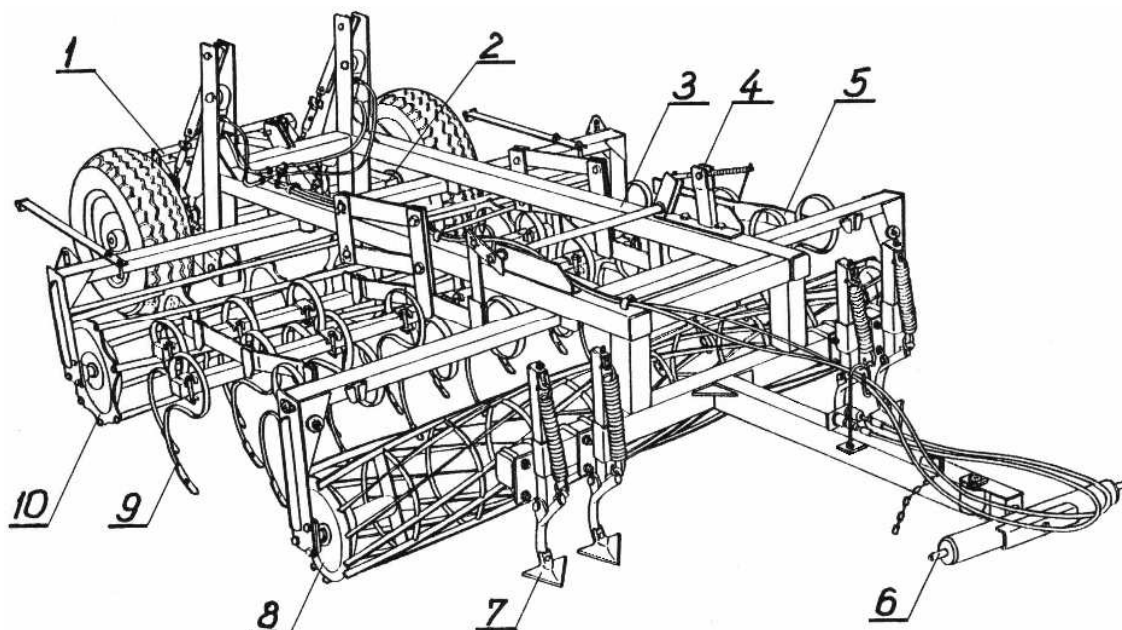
Посевно-обрабатывающий агрегат MARS XL 3.
